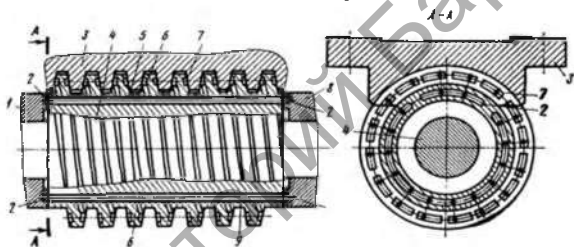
Схема гидростатической червячно-реечной передачи
